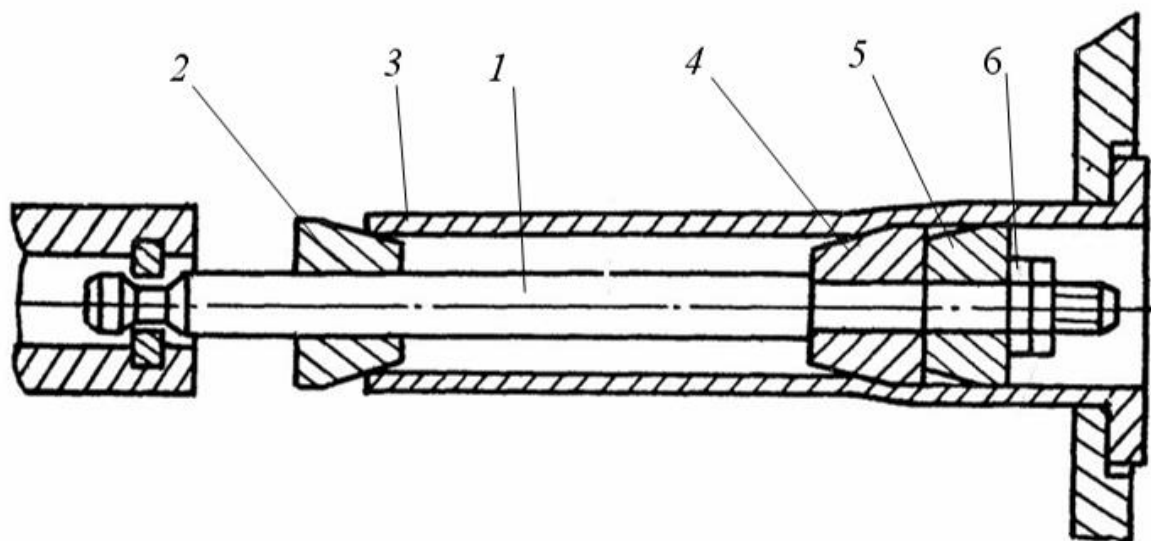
Схема обробки з використанням додаткового елемента, що підтримує вільний кінець заготовки й виключає неспіввісність інструмента та заготовки
